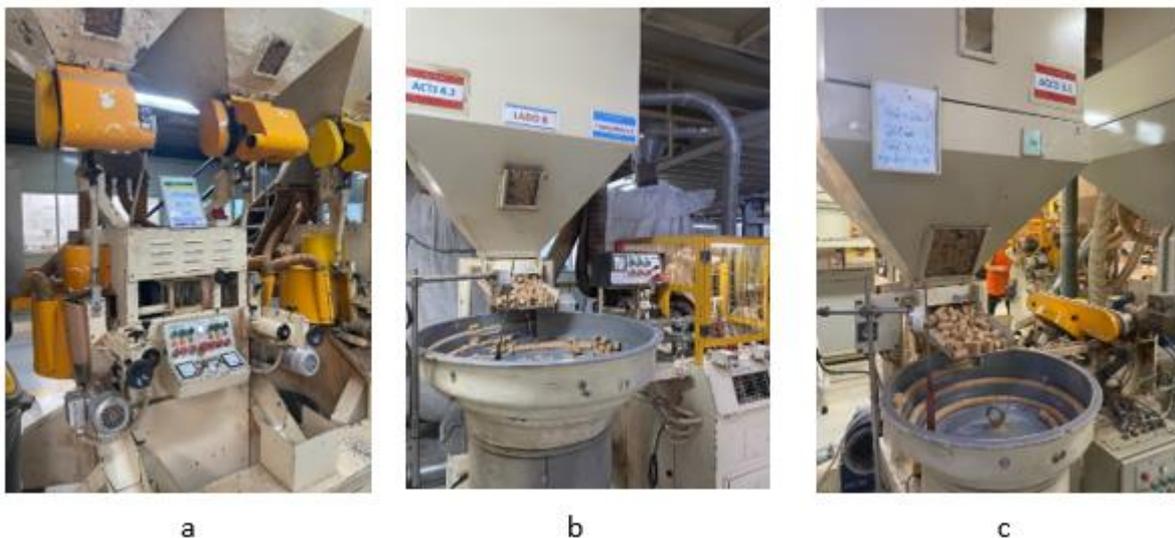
Equipamentos de Retificação: a) ponçadeira, b) topejadeira, c) chanfradeira
